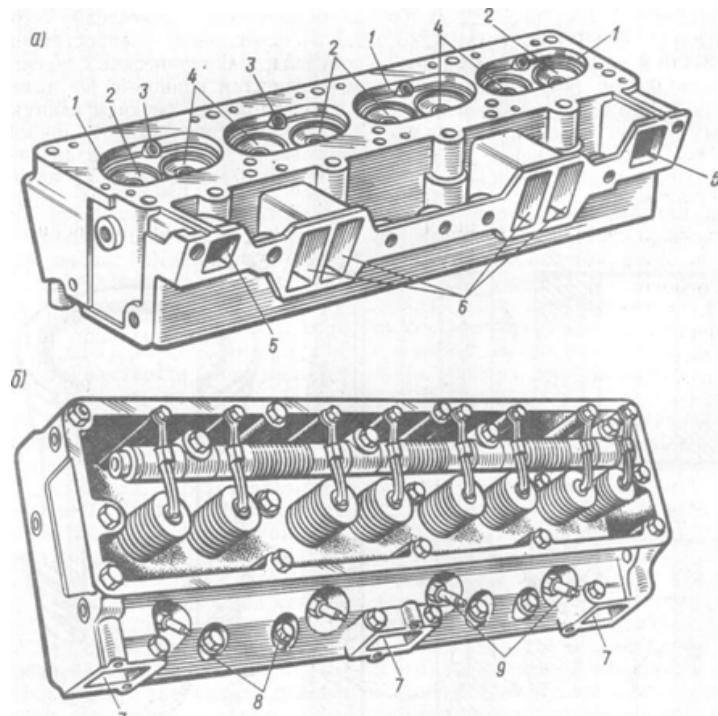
Головка цилиндров «V» - образного двигателя ЗИЛ-130
